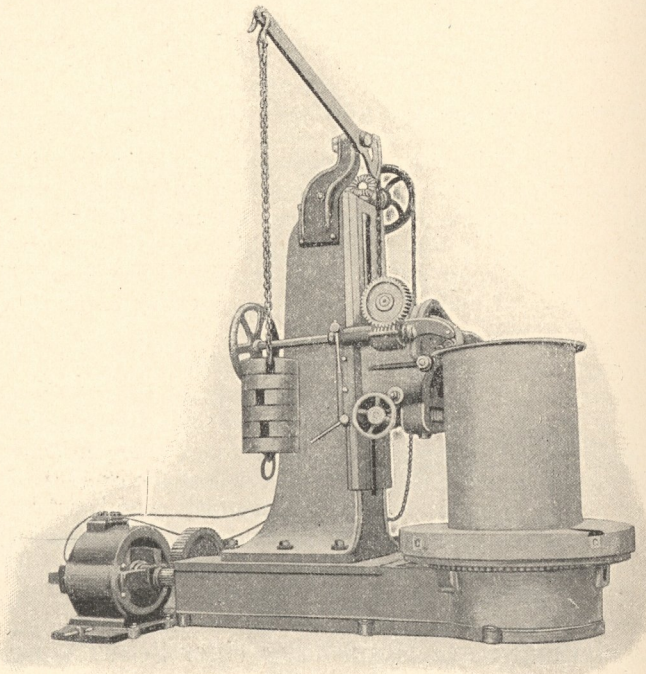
Börtelmaschine für Flammrohrschüsse.
